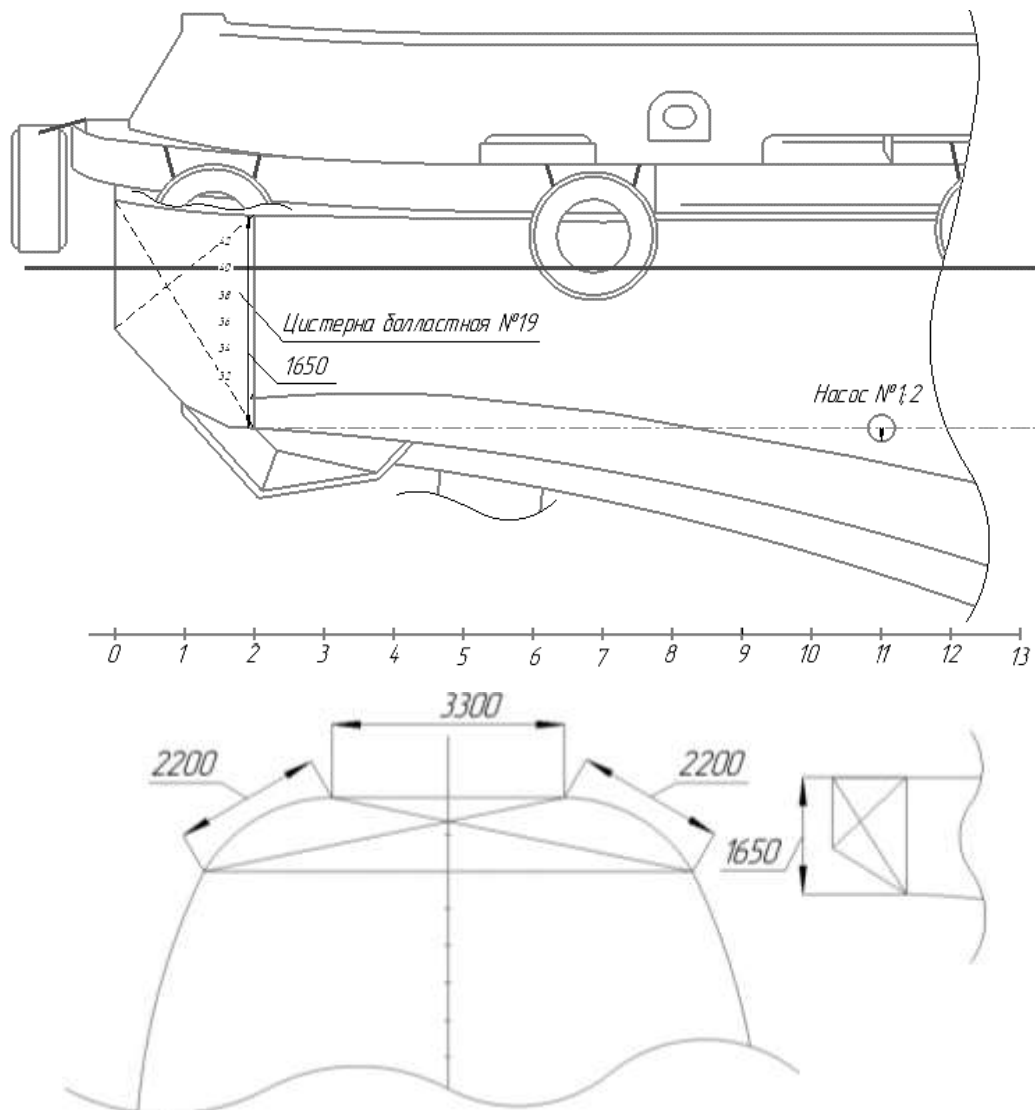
Расположение и размеры кормовой балластной цистерны
